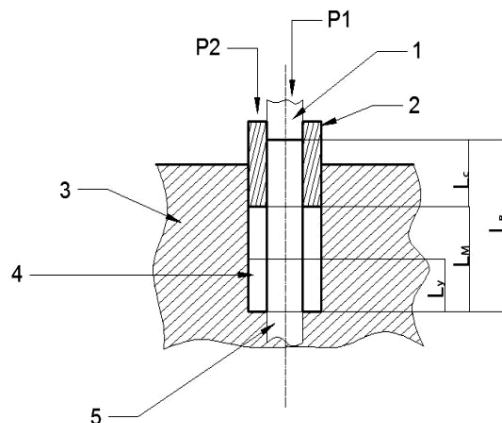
Схема однопереходной высадки поковки: 1 – пуансон; 2 – направляющая втулка-пуансон; 3 – матрица; 4 – полость штампа; 5 – стержневая заготовка
